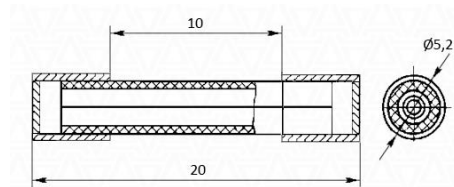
Габаритні розміри запобіжника ZH214-015
